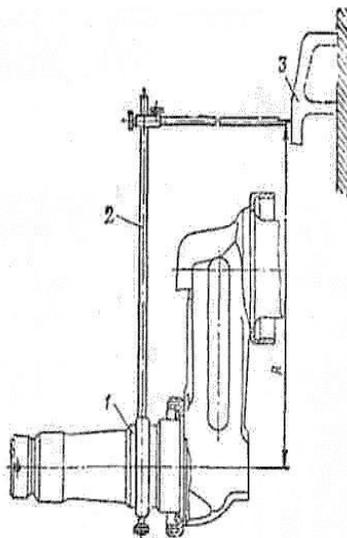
Установка приспособления ВП-СББ для выставки балансира на угол закрутки торсионного вала танка Т-72:
